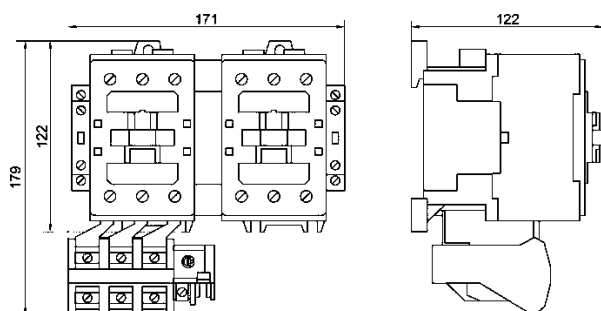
Пускатель реверсивный ПМ12-063 63А. Степень защиты - IP20.
